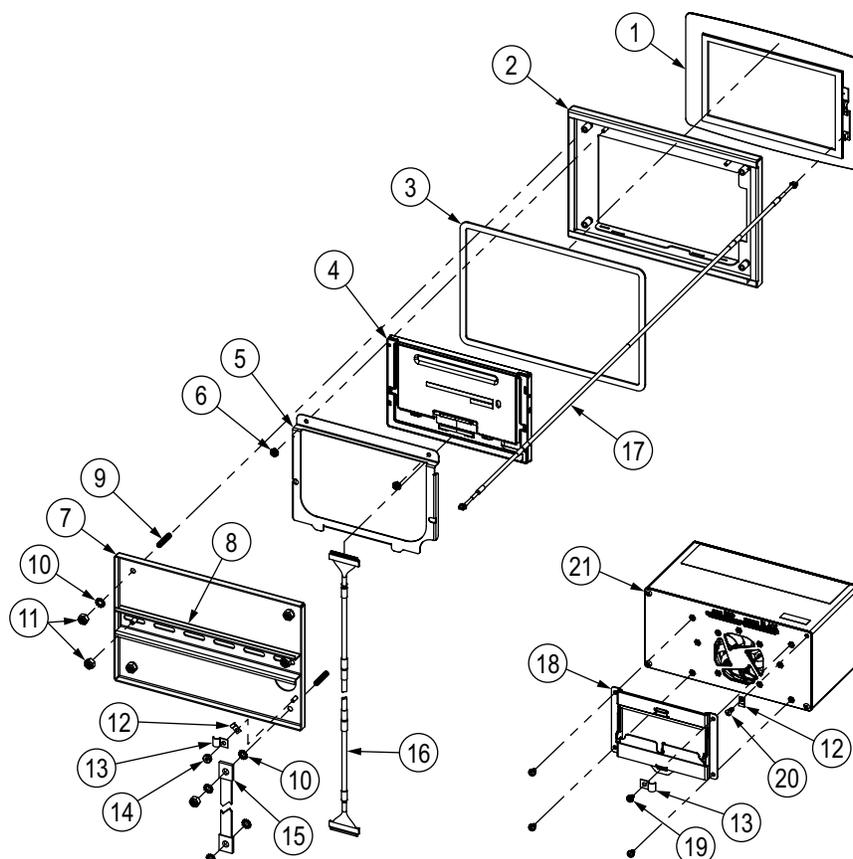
Componenti per la riparazione dell'indicatore da 7" con montaggio a pannello solo touch
